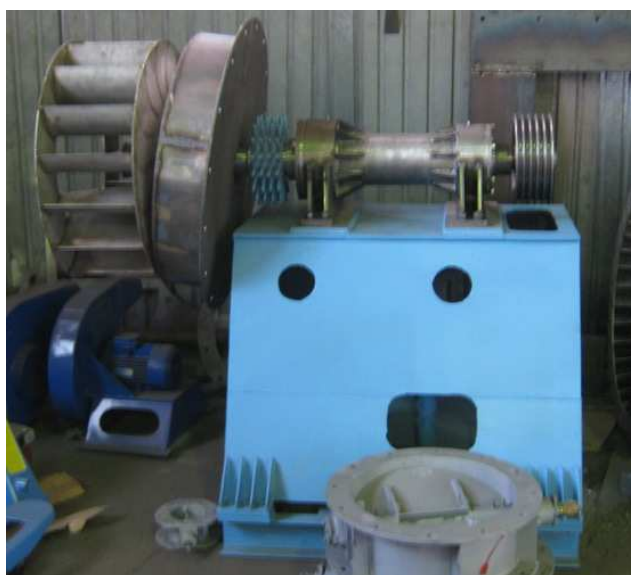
Жаропрочный циркуляционный печной вентилятор конструкции ОАО «ВНИИМТ»
